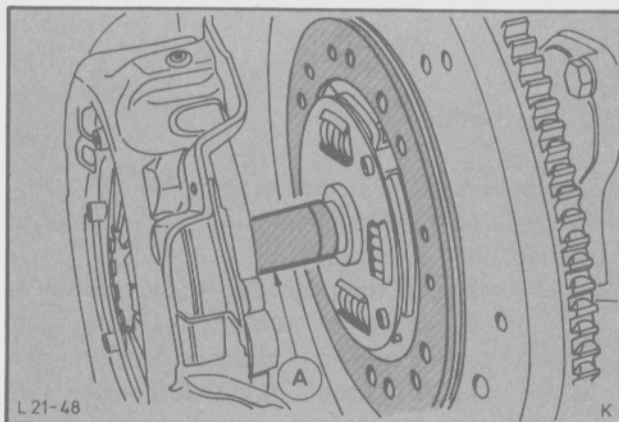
Centrado del disco de embrague con la herramienta T74G-7550-BAS.
